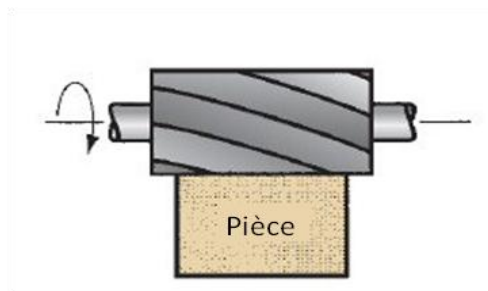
Procédés de fraisage : fraisage à vis et fraisage plan
